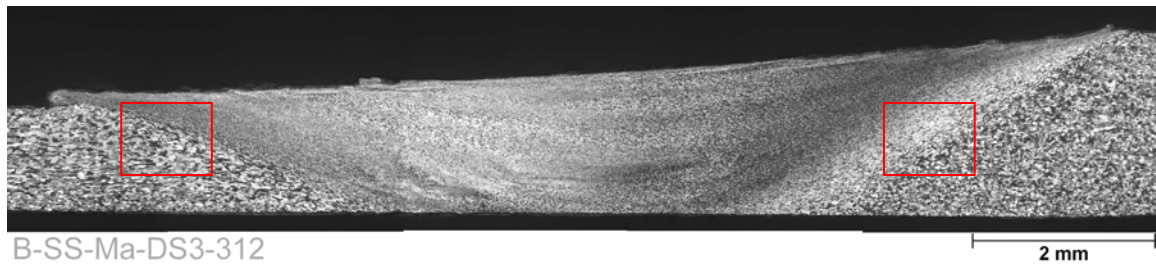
Macrografia de uma junta 6181 T4 soldada com 1 m/min. Ataque químico: Barker.
